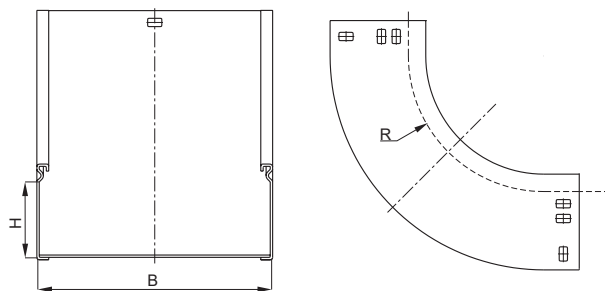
Поворот плавный 90° тип В10. Размеры для размещения кабеля / Figure С.2 – 90° smooth bend of B10 type. Dimensions for cable placement
